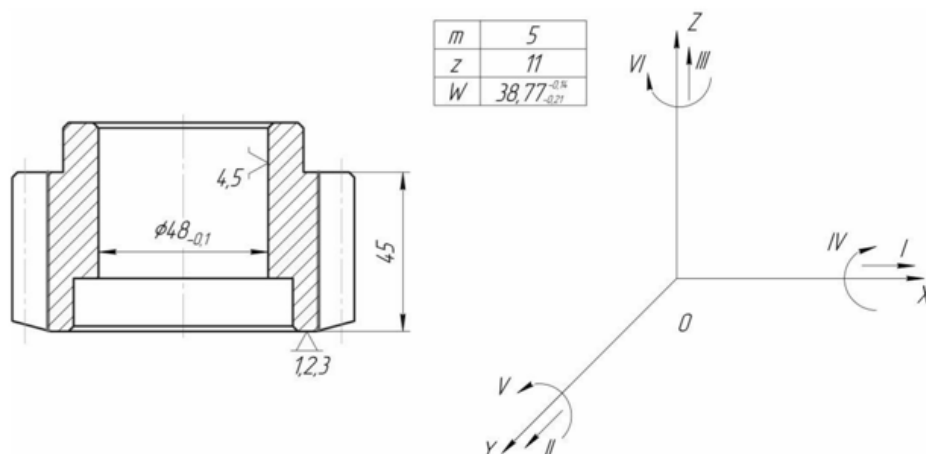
Схема базування для обробки на вертикально-фрезерному верстаті
